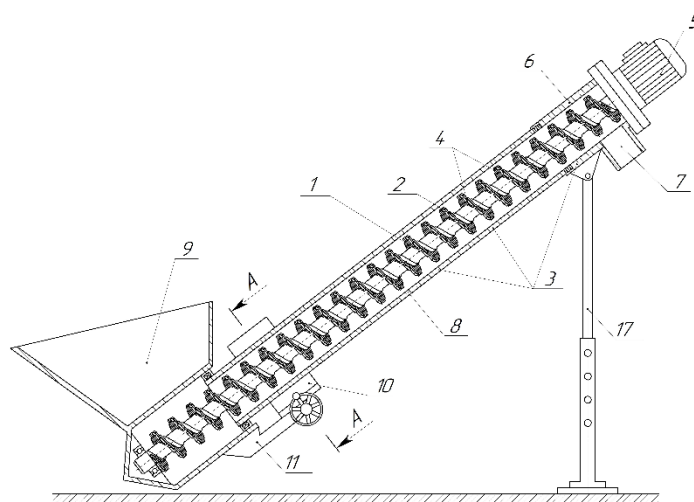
Конструктивна схема конвеєра-змішувача з обертovим кожухом:
